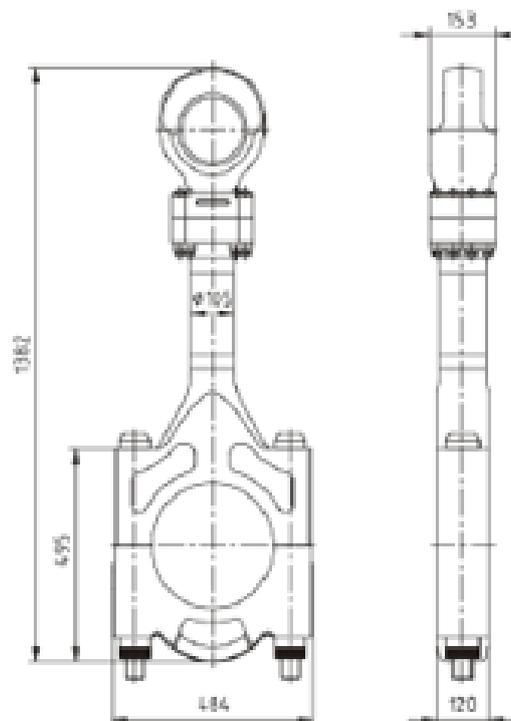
Dimensiones de la biela. Fuente: Manuel del motor del buque.
